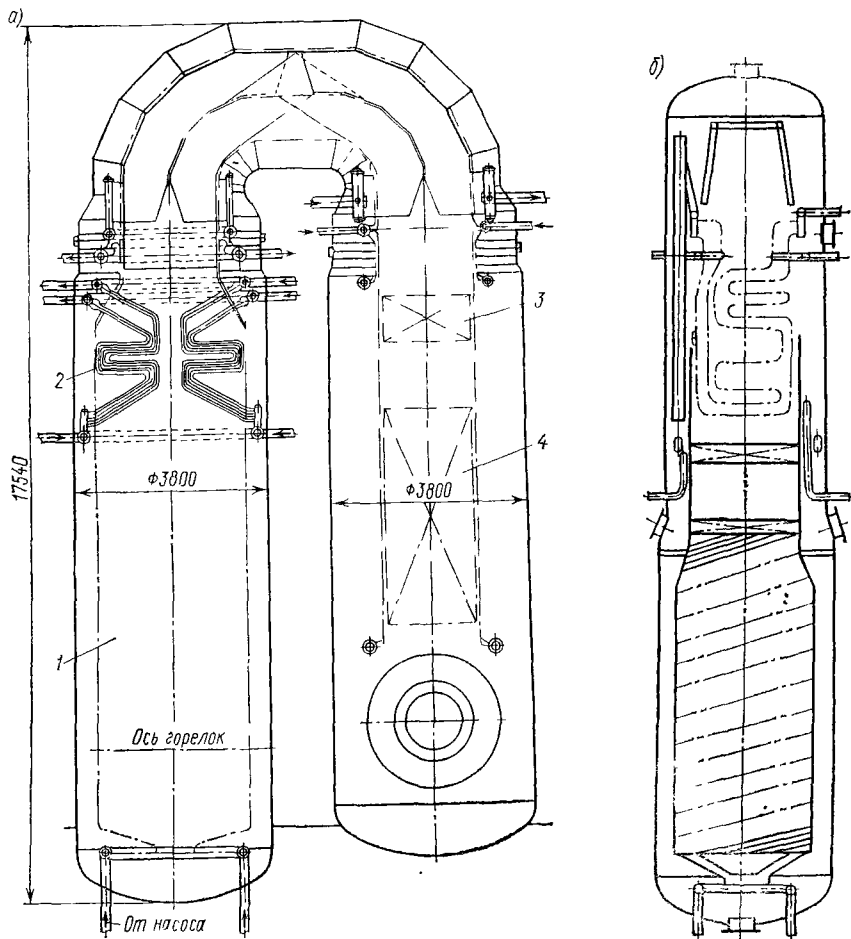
Корпус парогенератора ВПГ-450 с принудительной циркуляцией (а) и прямоточного типа (б) для парогазового блока мощностью 200 МВт: 1 — топочная камера; 2 — ширмовая поверхность нагрева; 3 — I ступень промежуточного пароперегревателя; 4 — II ступень пароперегревателя
